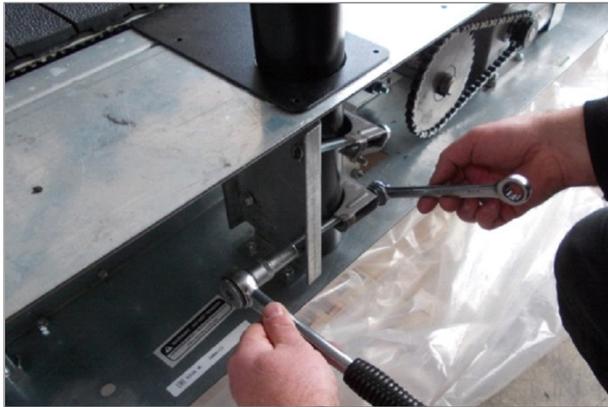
Montage Pro/ProXL, Geländerbefestigung 2
